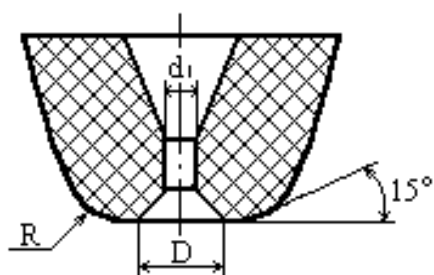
Капилляр для термокомпрессионной сварки
